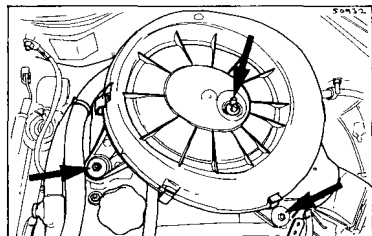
Болты и гайки крепления воздушного фильтра (указаны стрелками)
